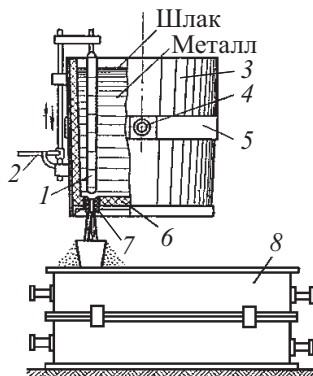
Стопорный крановый ковш для разливки стали:
